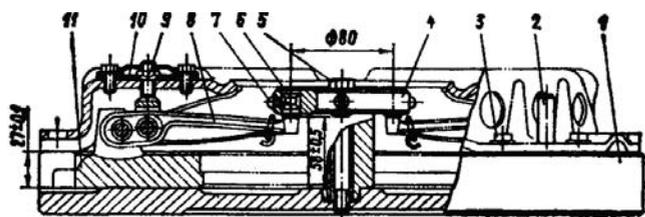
Приспособление для сборки нажимного диска с кожухом в сборе: 1 — подставка; 2 — штифт; 3 — болт крепления кожуха сцепления; 4 — оправка; 5 — болт крепления оправки; 6 — упорный сухарь; 7 — винт; 8 — отжимной рычаг сцепления; 9 — регулировочная гайка; 10 — опорная пластина; 11 — нажимной диск сцепления
